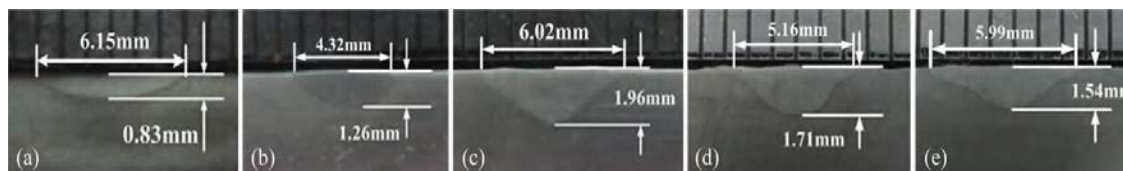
Поперечное сечение сварных швов при разных диаметрах излучателя:
